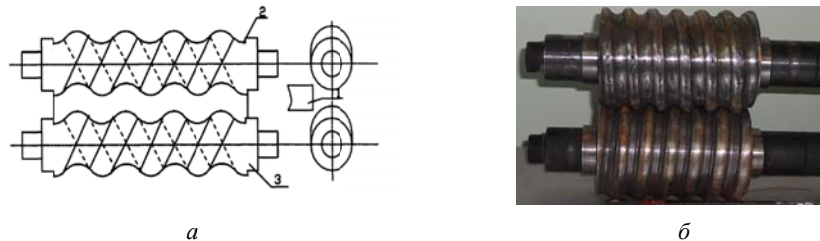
Схема прокатки в валках с винтообразными рабочими поверхностями.
